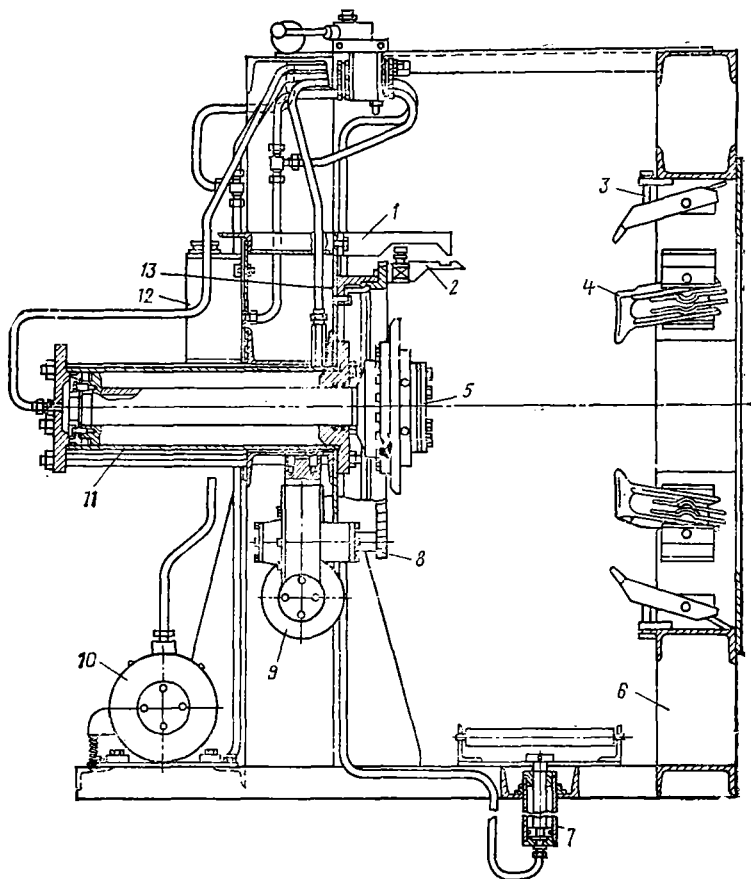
Стенд для демонтажа и монтажа шин грузовых автомобилей: 1—упоры; 2—съемник замочного кольца; 3—винты; 4—лапы; 5—пневматический патрон; 6—рама; 7—гидравлический подъемник; 8—шестерня; 9—редуктор; 10—гидравлический привод; 11—гидравлический цилиндр; 12—бачок; 13—обечайка
